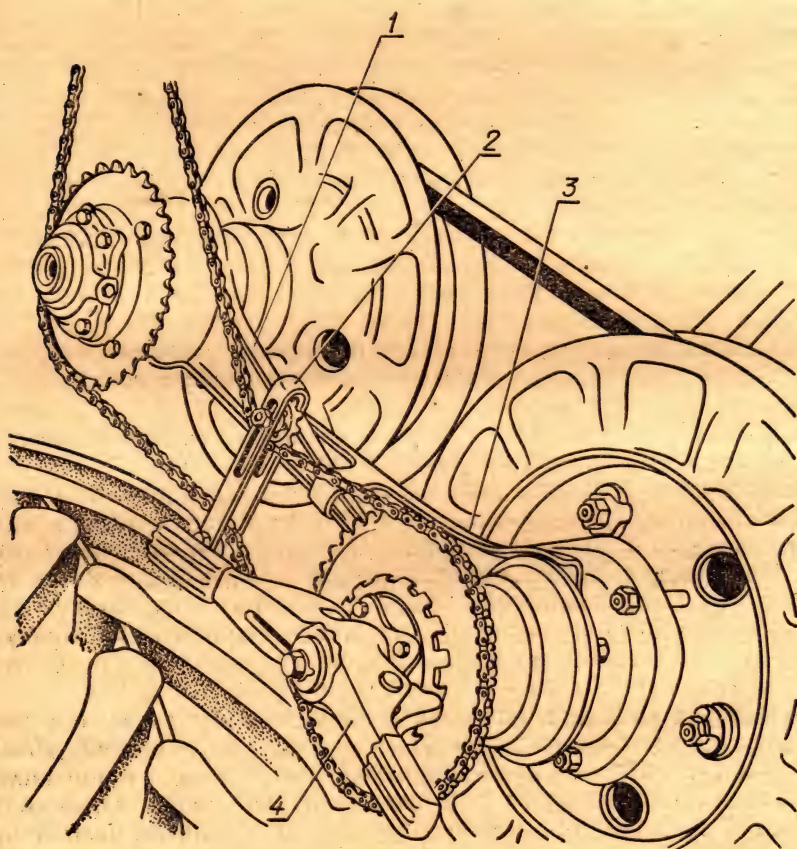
Общий вид механизмов регулирования оборотов комбайнов СК-5 и СК-6:
